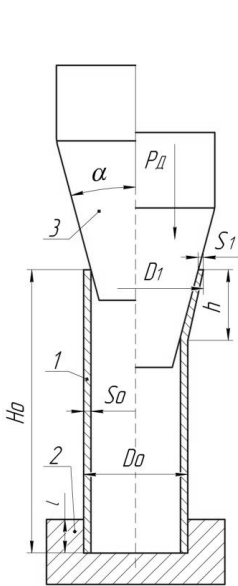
Схема відкритої роздачі трубчастої заготовки
